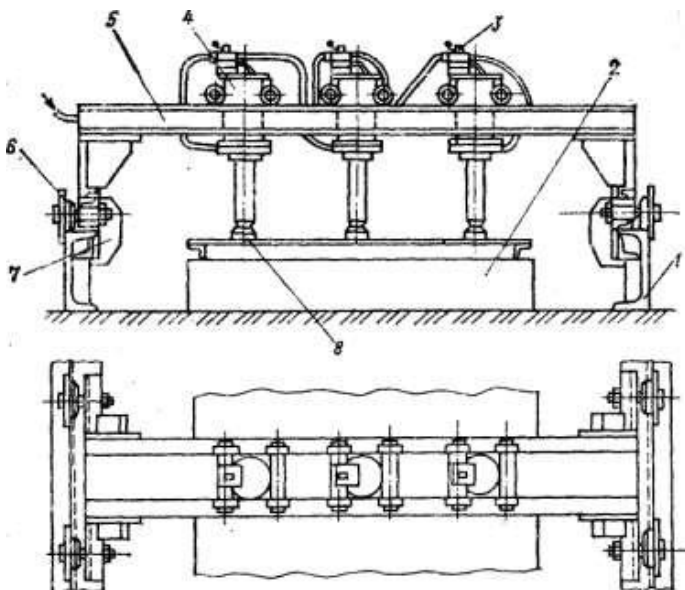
Стенд для сборки и сварки полотнищ
